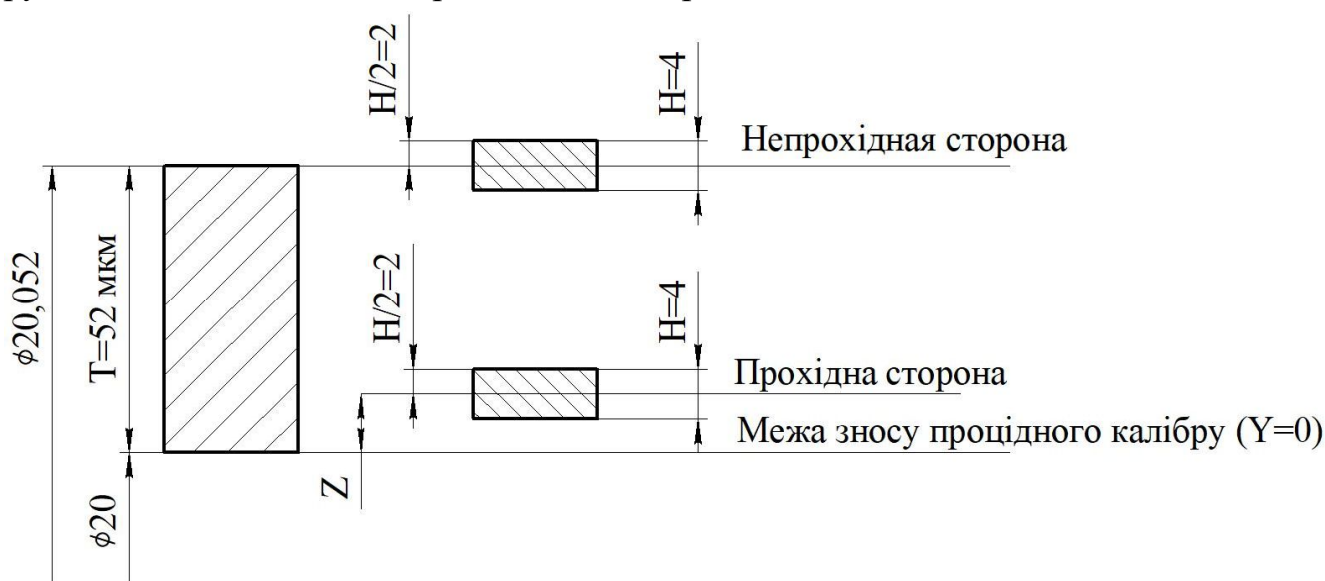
Схема розташування полів допусків граничних калібрів
